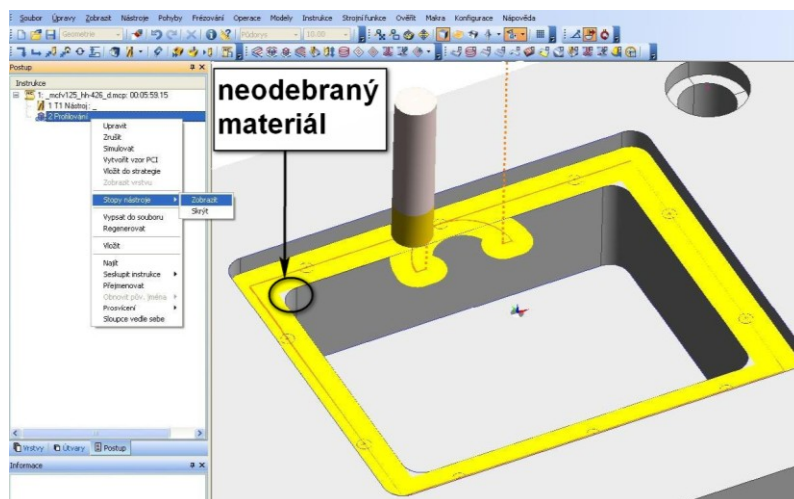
Porovnání modelu s obrobkem (MasterCAM)
